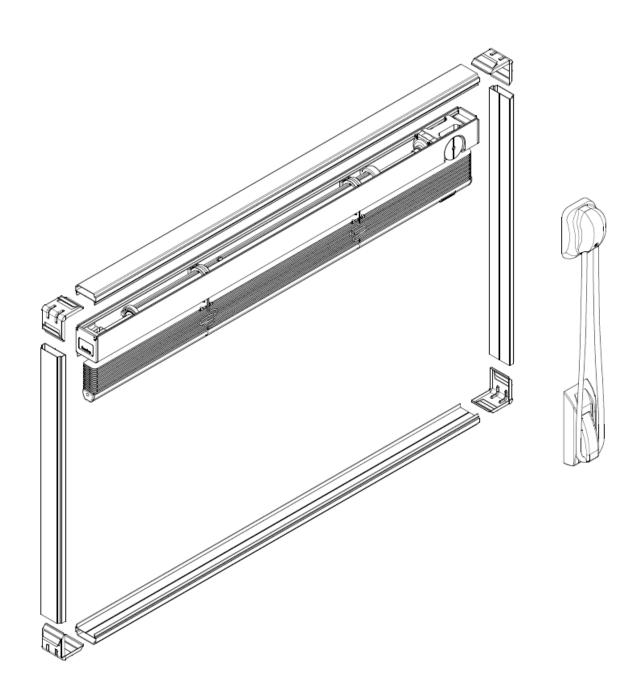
Vue d'ensemble éclatée - Store en position relevée
